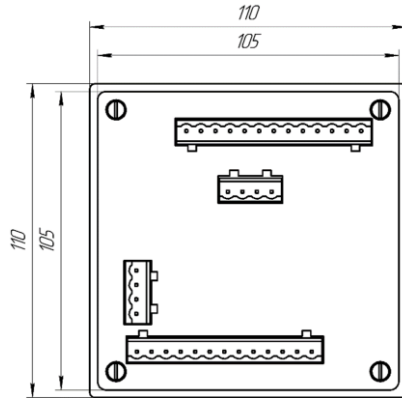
Габаритный чертеж устройства серии МСТ. Вид сзади
